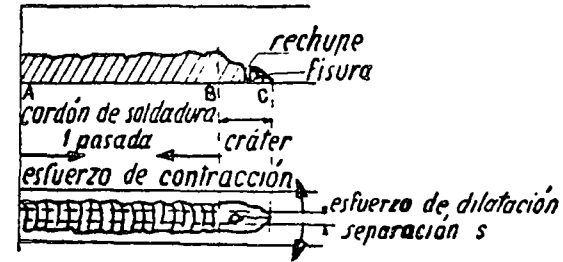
Interpretación del agrietamiento en el cráter terminal de una soldadura por arco.
